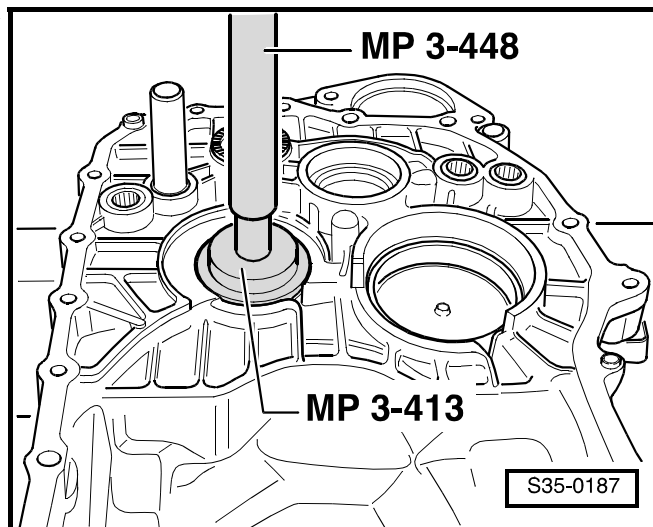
Извлечение внутреннего кольца конического роликоподшипника
